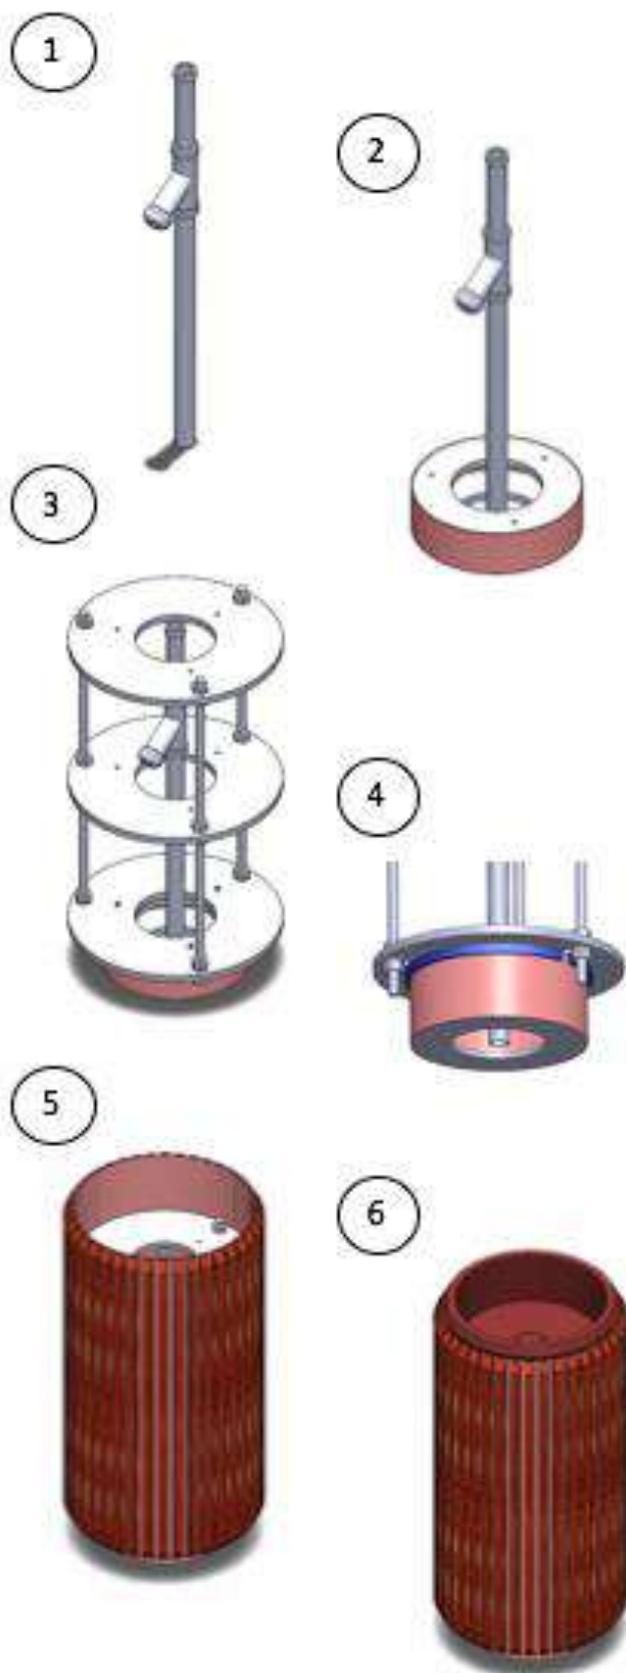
Proceso de montaje del mueble de baño Taglio.
